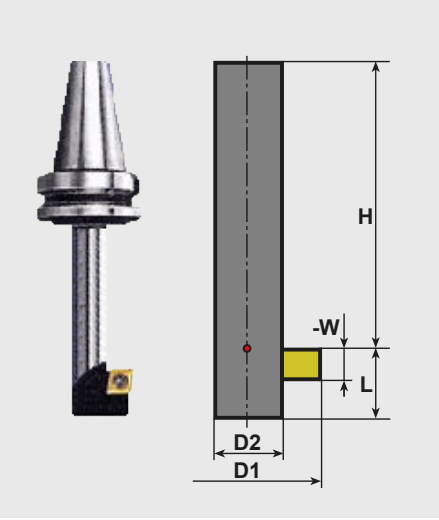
Werkzeugbeschreibung TOOL/BBAR Bohrstange
